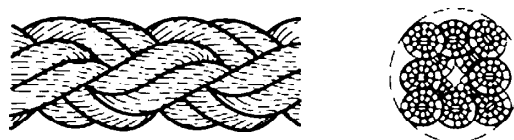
Forme d'un cordage tressé à 8 torons (type L)
